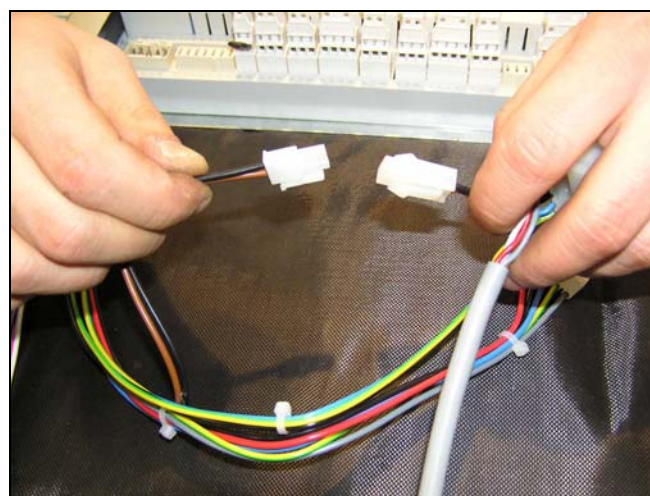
Verbinden Sie das Brenneranschlusskabel mit dem Reset-Schalter im Kesselschaltfeld. (Stecker mit schwarzer und brauner Litze)
